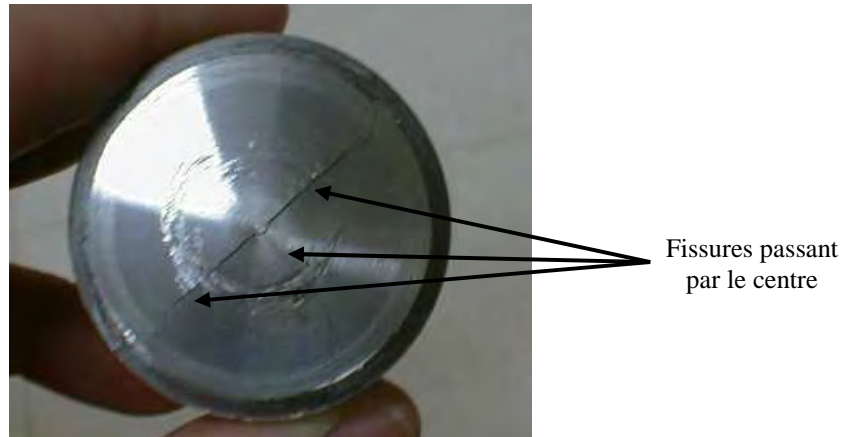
Fissures typiques présentes sur la face extérieure du poussoir forgé ; 3 fissures se rejoignant au centre
